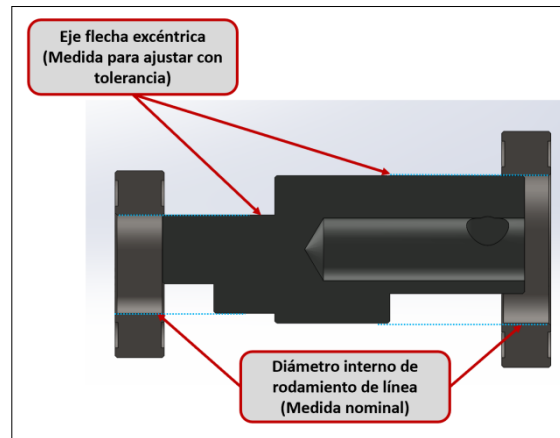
Vista de sección transversal ensamble de flecha excéntrica con rodamientos.
